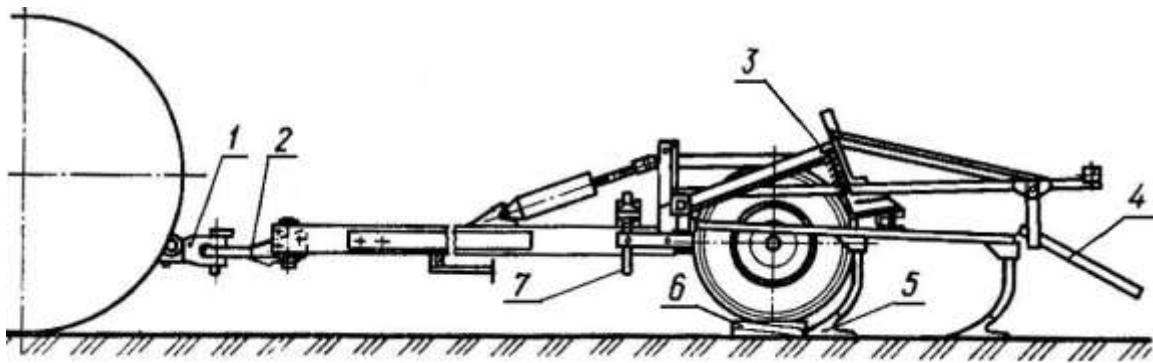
Схема встановлення культиватора на задану глибину обробітку:
